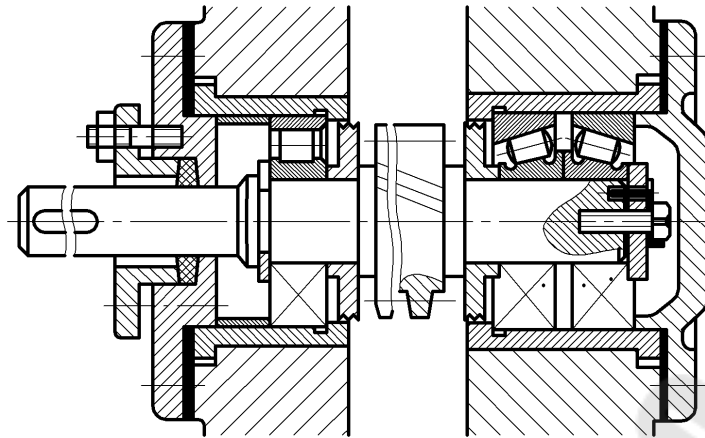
Подшипниковый узел со сдвоенными коническими роликоподшипниками и роликовым подшипнике («плавающая» опора)
